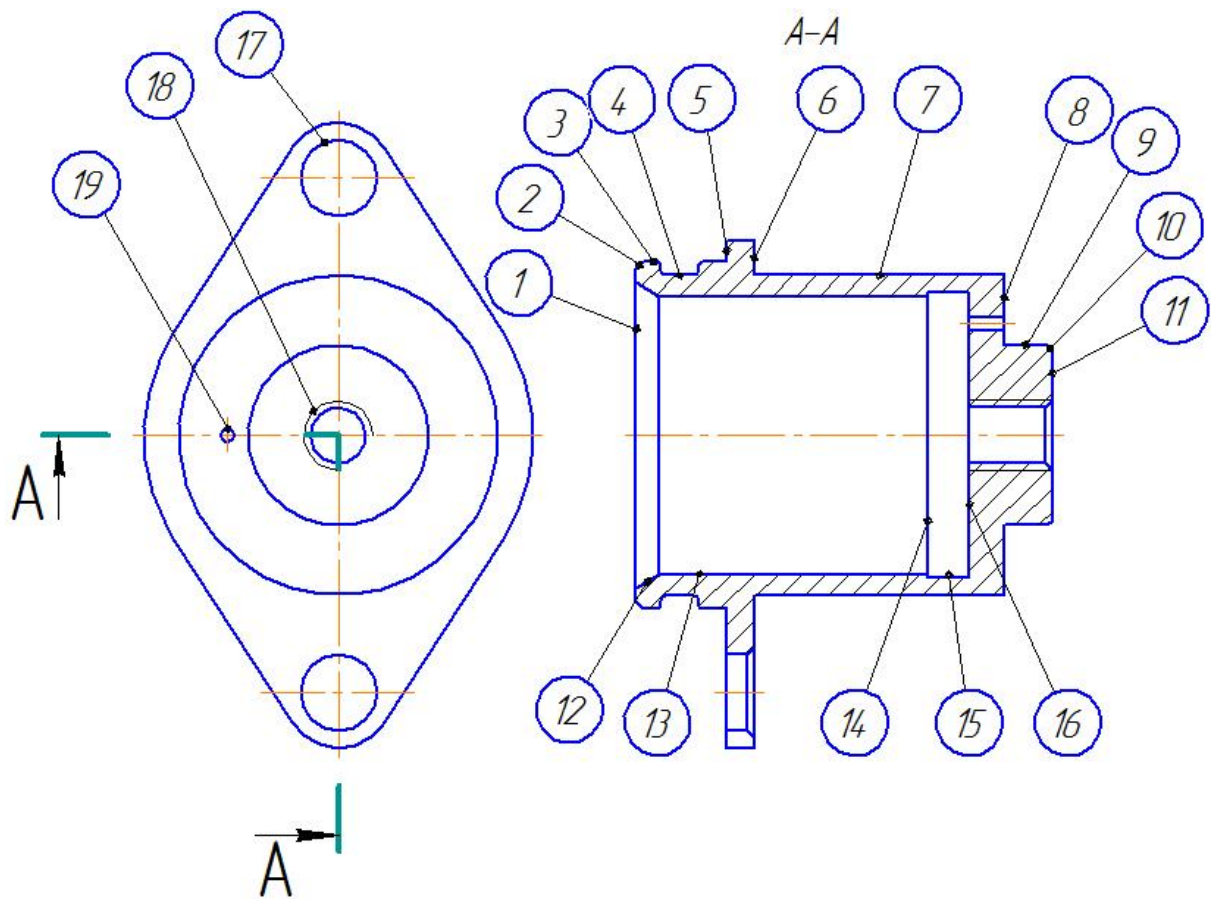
Эскиз детали с номерами обрабатываемых поверхностей
